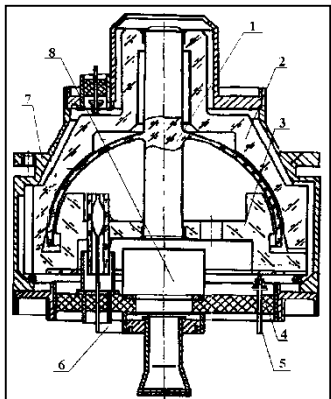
Конструкция ВТГ: 1,2,3–кварцевые резонатор и корпуса; 4–керамическая колодка; 5,6–гермовыводы; 7–кожух; 8–насос
